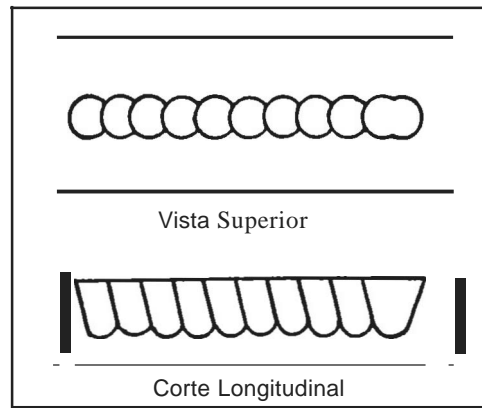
SOLDADURA OBTENIDA POR EL PROCESO TIG CON ARCO PULSADO
